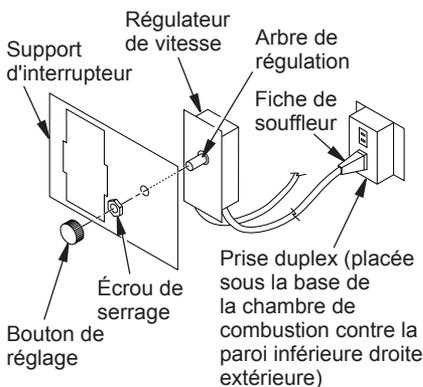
Raccordement du régulateur de vitesse à la chambre de combustion
